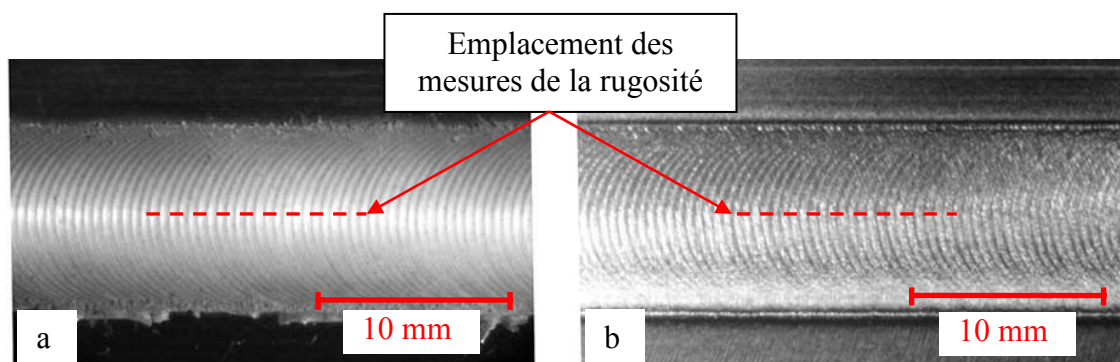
Emplacement des mesures de rugosité de surface (a) joint brut de soudage, (b) joint brossé à 5 mm/s.
